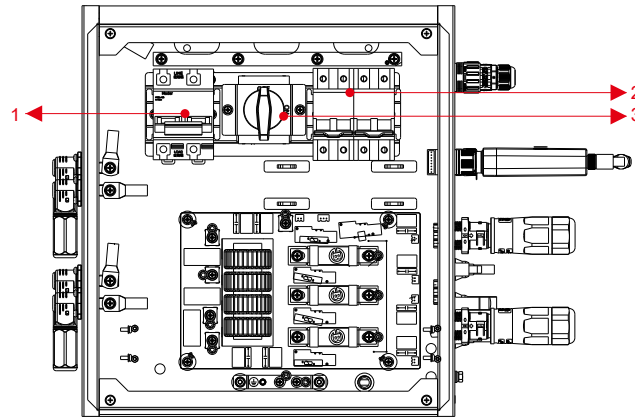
Pièces de la boîte de câble sans couvercles – Vue de face
